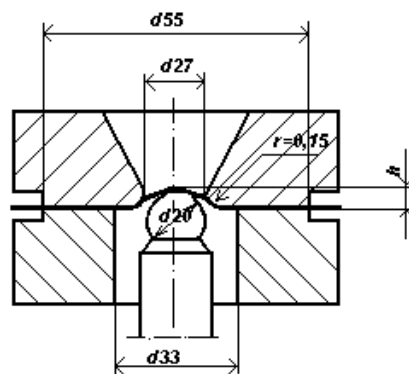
Схема испытания по «Эриксену» на глубину формовки лунки.
